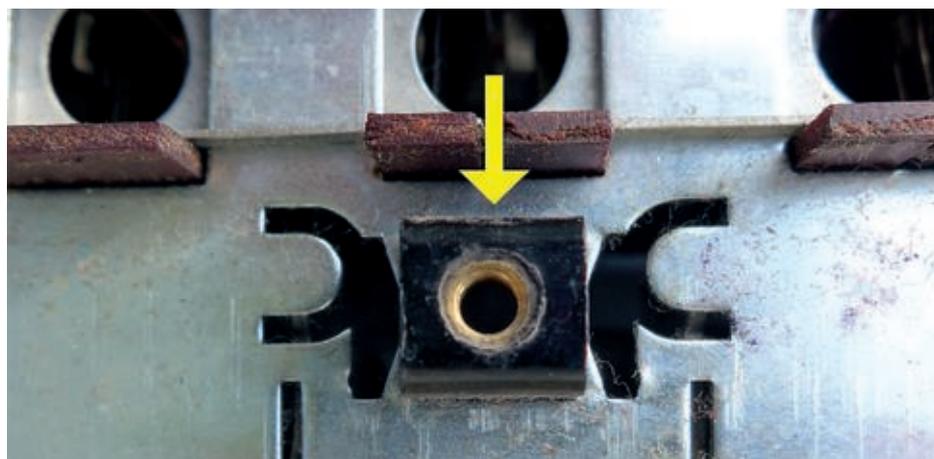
Die Fassung der Schraube der abgewinkelten Rückwand am Boden ist in einem Isolierblock befestigt.
